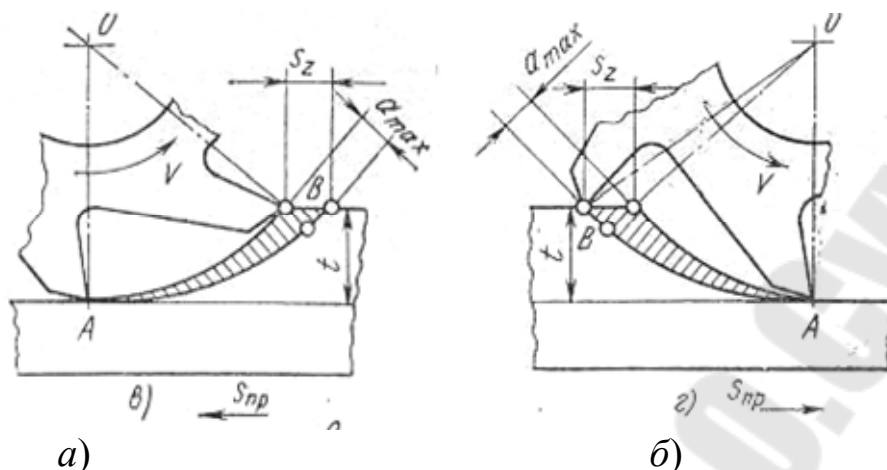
Схема встречного (а) и попутного (б) фрезерования
